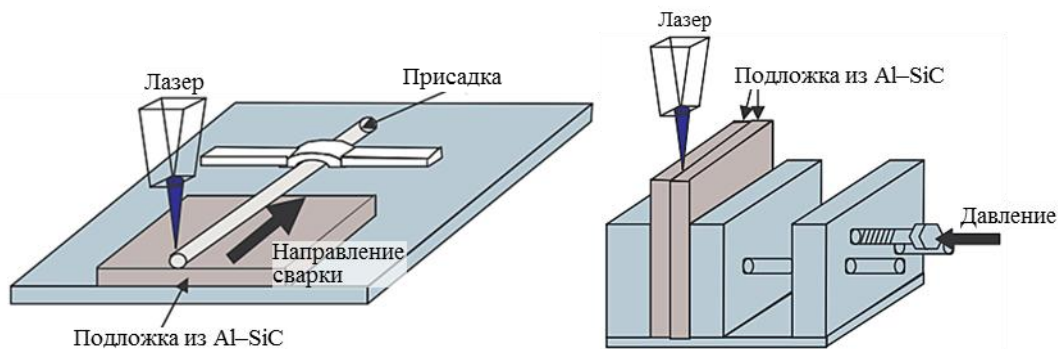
Схема сварки (а) и пайки (б) алюминиевых МКМ
